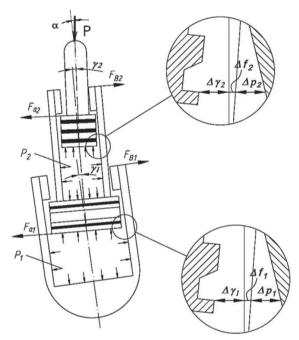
Схема формирования уплотняемых зазоров при перекосах штоков и цилиндров первой и второй ступеней раздвижности: α — угол установки гидростойки в крепи; γ_1 , γ_2 — углы перекоса штока и цилиндра первой и второй ступеней; p_1 , p_2 — давление рабочей жидкости в рабочих цилиндрах первой и второй ступеней; P — внецентренная внешняя сила; $F_{\rm a1}$ и $F_{\rm B1}$, $F_{\rm a2}$ и $F_{\rm B2}$ — дополнительные силы, возникающие из-за перекоса первой и второй ступеней; $\Delta\gamma_1$, Δf_1 и Δp_1 , $\Delta\gamma_2$, Δf_2 и Δp_2 —зазоры между поршнем и рабочим цилиндром, вызванные, соответственно, полями допуска на изготовление, дополнительными силами из-за перекоса и воздействия давления рабочей жидкости в первой и второй ступенях
